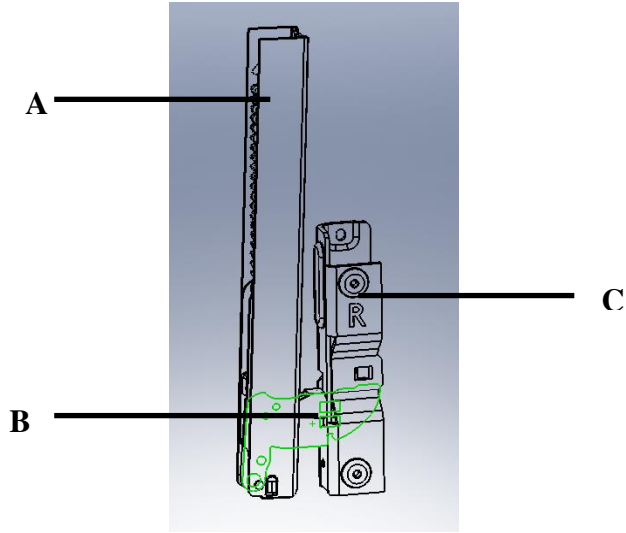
Mevcut durumdaki kuvvet akış şeması
